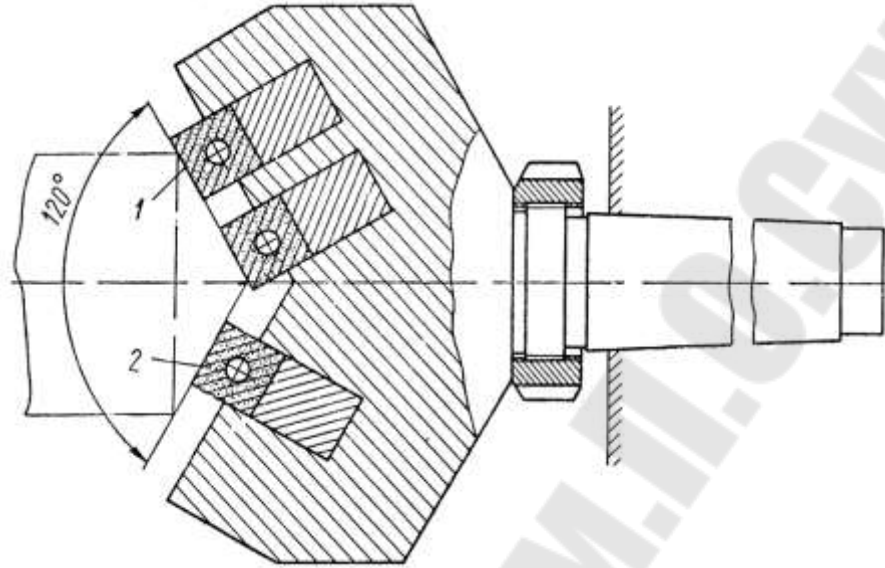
Эскиз резцового блока для обработки конических торцов (угол  $120^\circ$ )
